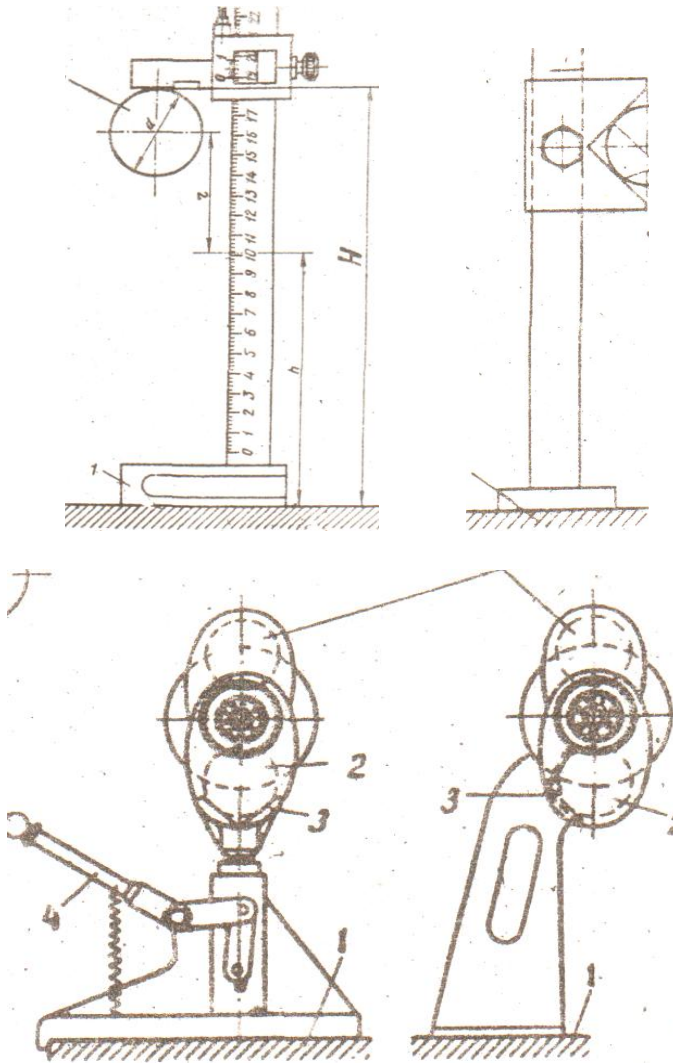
Приспособление для установки коленчатого вала при шлифовании шатунных шеек; а - штангенрейсмус; б - шаблон с передвижной призмой; в - шаблон для установочного вала в вертикальной плоскости; г - жесткий шаблон для установки вала в горизонтальной плоскости; 1 - верхний стол станка; 2 - шейка вала; 3 - призма; 4 - ручка
